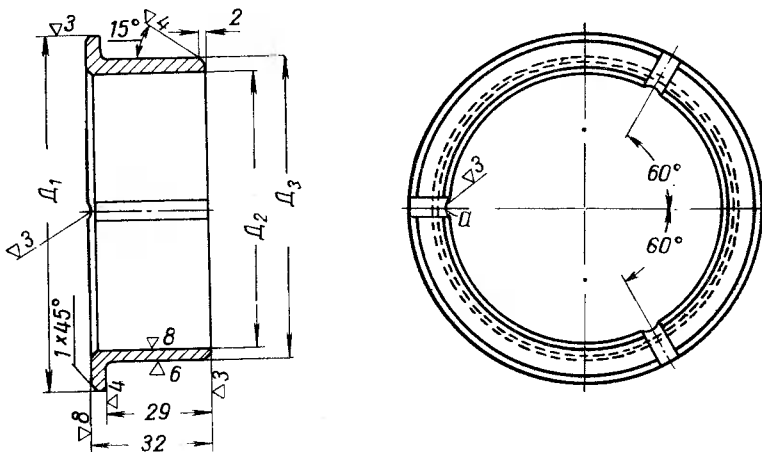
Втулки шестерен привода среднего и заднего мостов промежуточного вала
